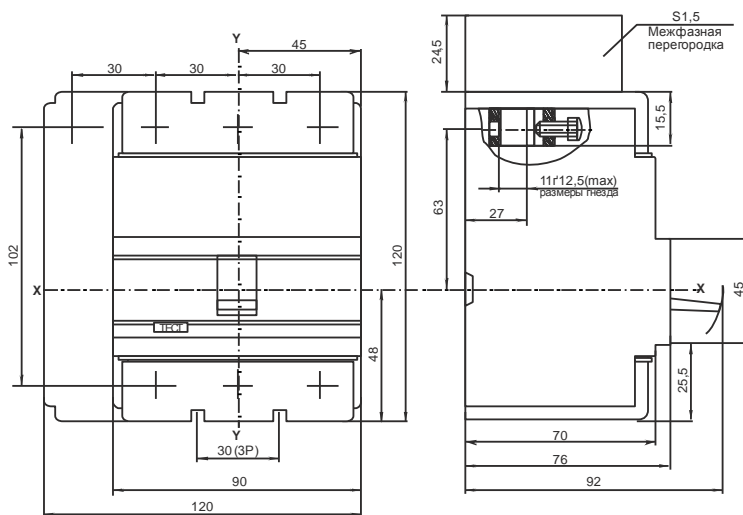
Габаритные и установочные размеры выключателя ВА88-33
